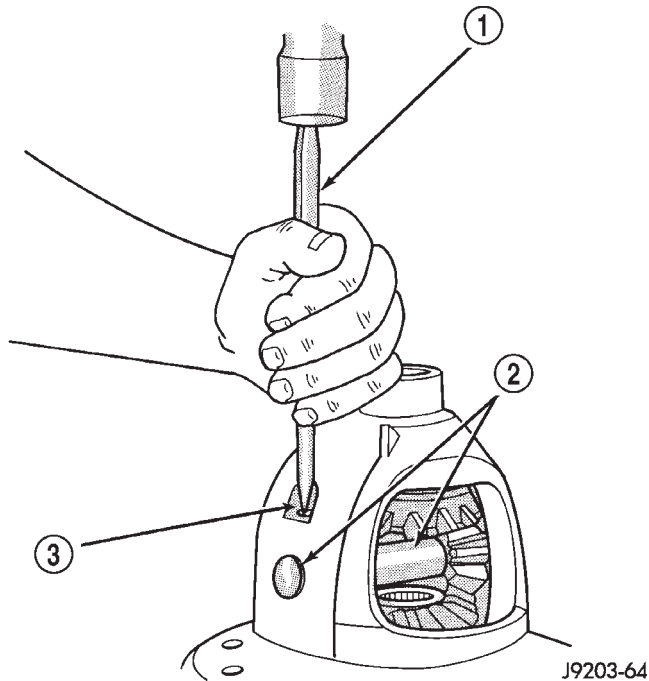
PASADOR DE RODILLO DEL EJE ENGRANADO
